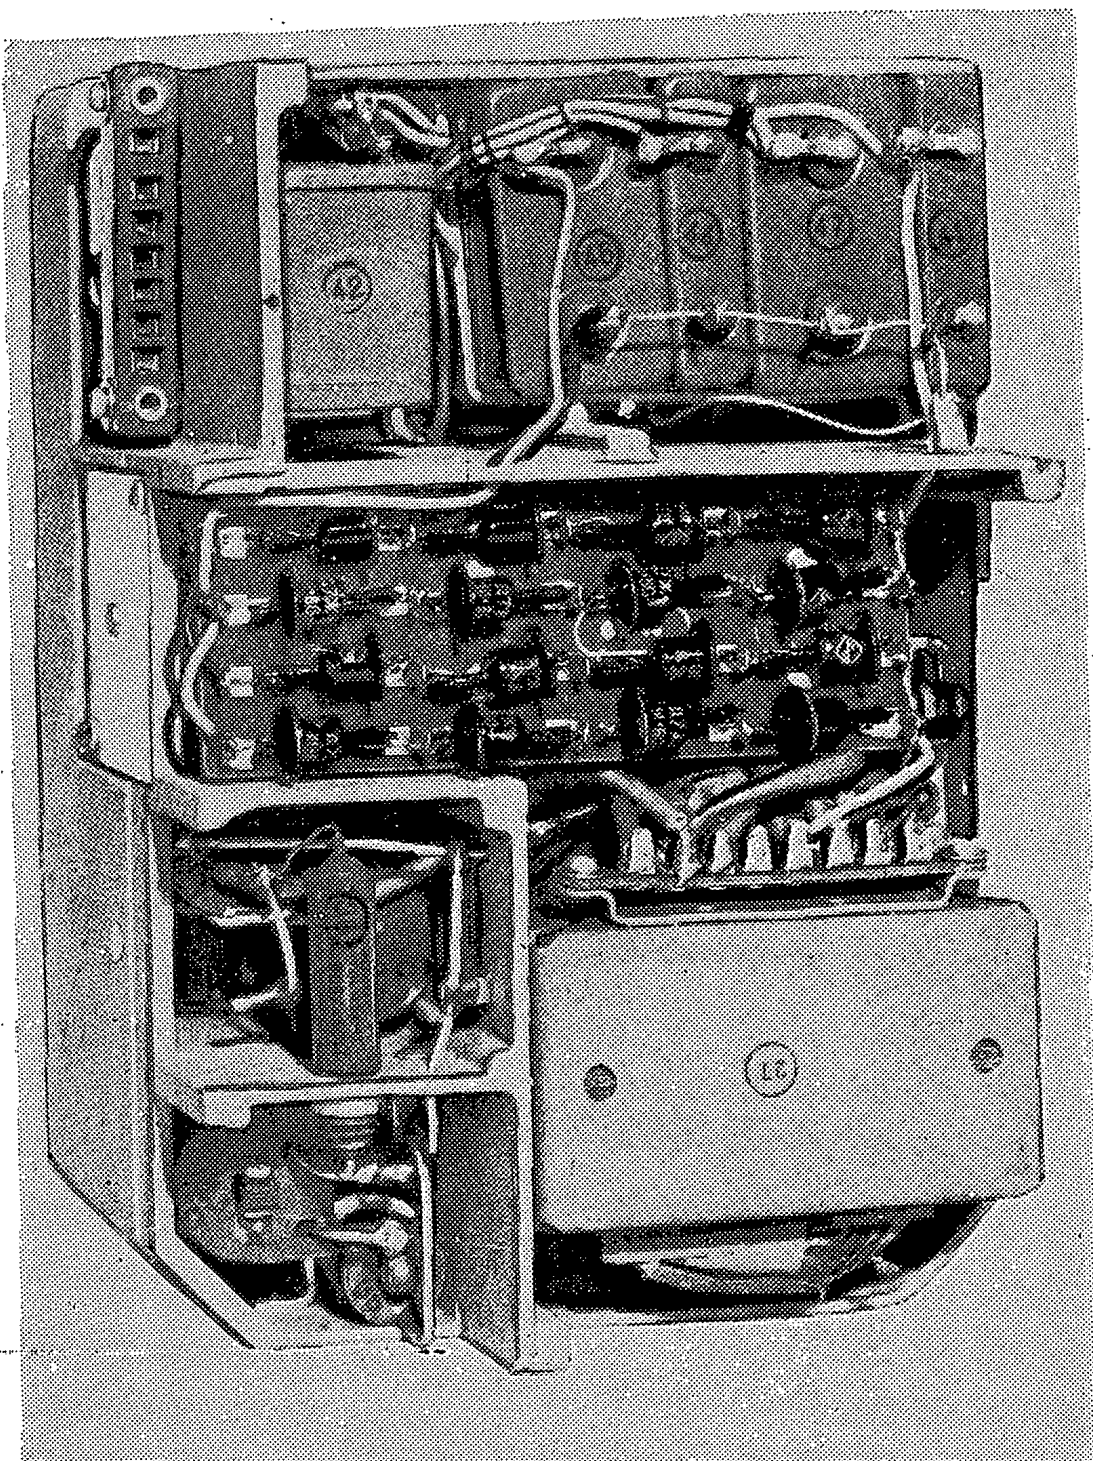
Расположение деталей и монтажа блока вибропреобразователя.
